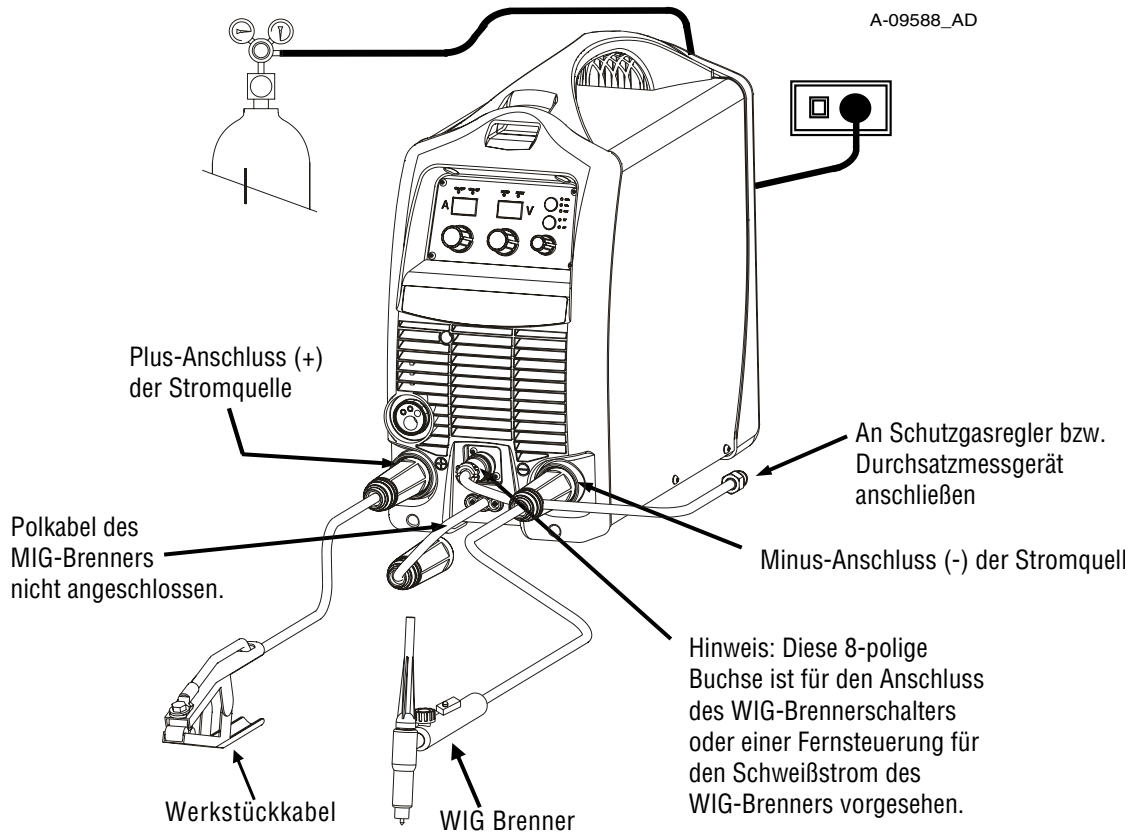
Konfiguration für WIG-Schweißen
